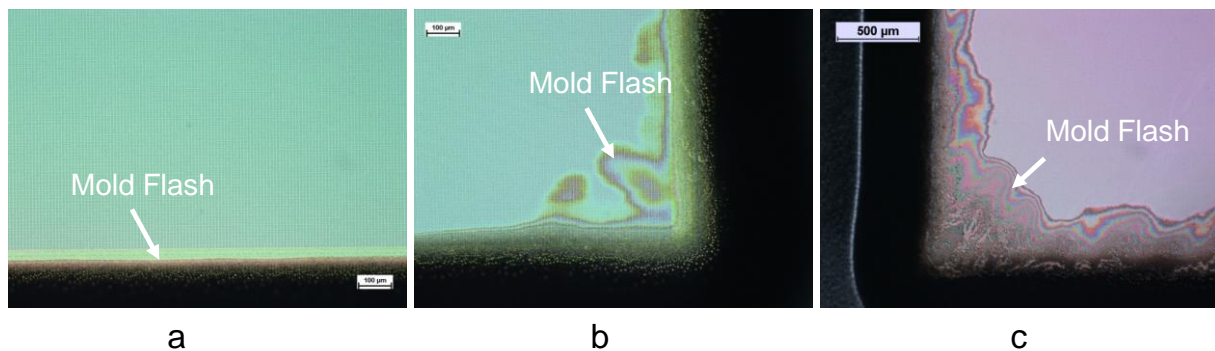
a) zeigt die ideale Form des Mold Flashes, die beim FAM-Prozess auftreten kann, b) veranschaulicht einen weitläufigen klaren Mold Flash und c) stellt einen Mold Flash mit einem Übergang vom gemischten zum entmischten Zustand dar.
